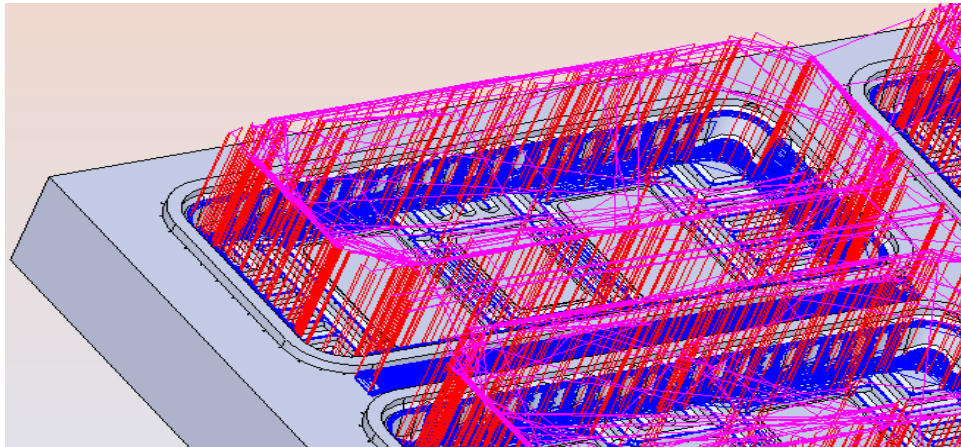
Desbaste de restos con herramienta $\varnothing 6$ mm.
